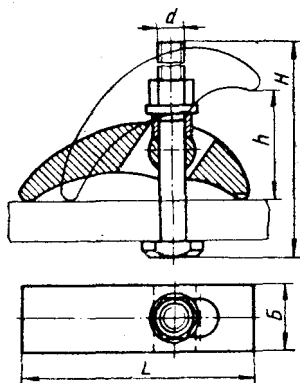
Агрегированный узел — прихват винтовой шарнирный
